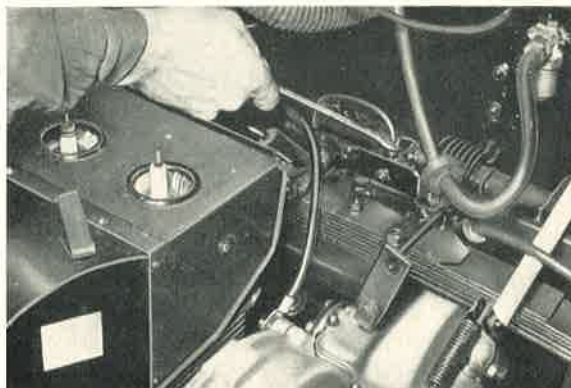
Die Öldruckleitung für die Bremse wird oben am Winkelstück abgeschraubt und leicht abgelenkt.
